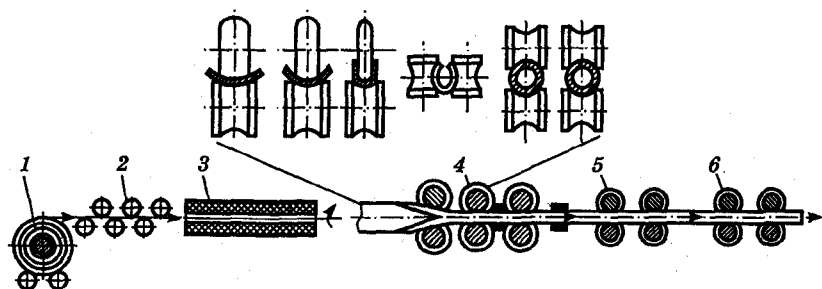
Схема производства труб непрерывной печной сваркой
